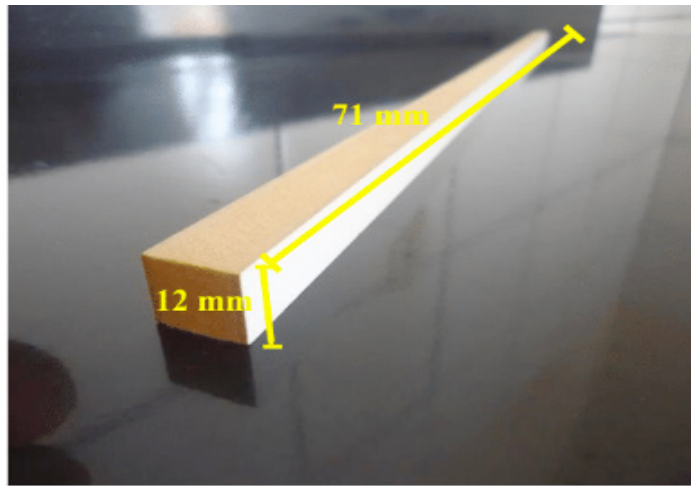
Resíduo Sólido (apara - 71 mm x 12 mm) originado da etapa de corte. Marabá – PA.
